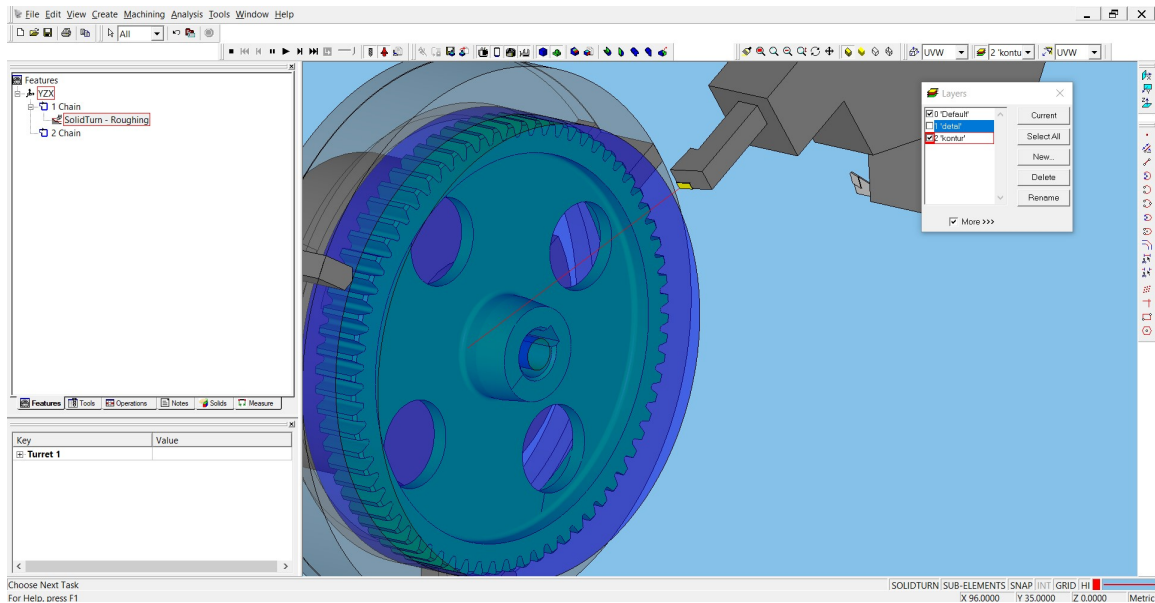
Траєкторія руху металорізального інструменту при обробленні контуру
